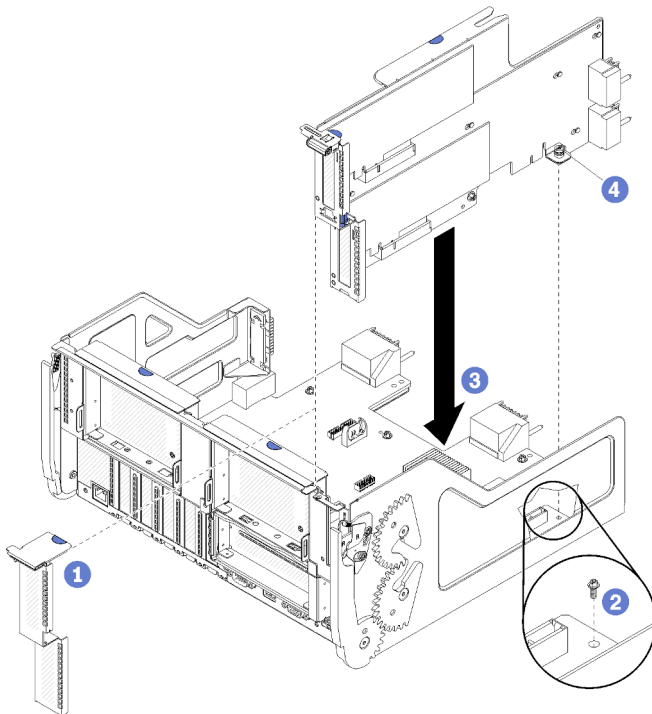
Instalación de la expansión para las ranuras 16 y 17
